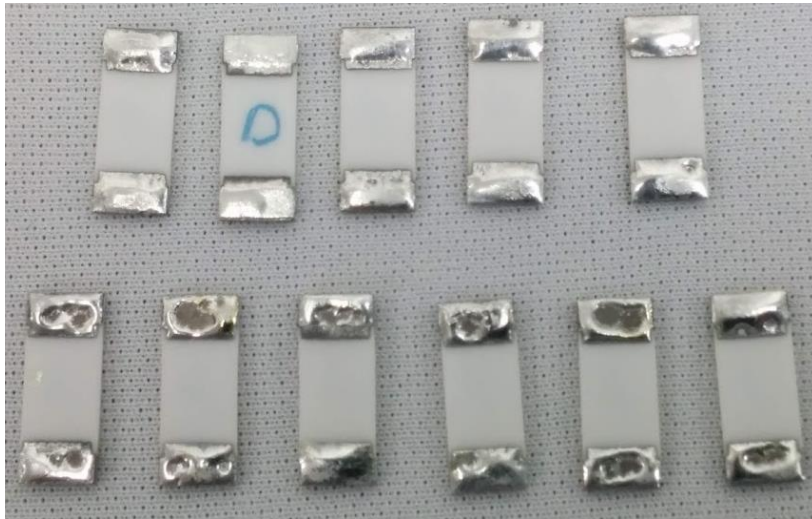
Representación de soldabilidad. En la parte superior se observan piezas con correcta soldabilidad, la cuales muestran una superficie de soldadura uniforme. En la parte inferior se muestran piezas con mala soldabilidad, la cuales muestran una superficie cubierta con soldadura irregular. Autoría propia, 2019.
